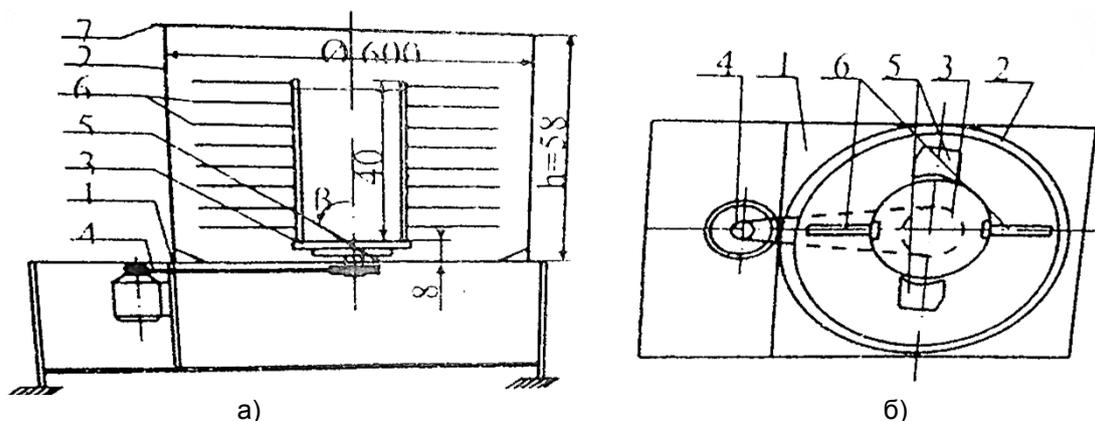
Схема лабораторного бескаткового центробежного смесителя селективного перемешивания ПГС: а) поперечный разрез; б) вид сверху со снятой крышкой; 1 – основание; 2 – цилиндрическая чаша; 3 – ротор с нижним приводом; 4 – электродвигатель привода; 5 – плужки с регулируемым углом атаки; 6 – рассекатели; 7 – крышка чаши
